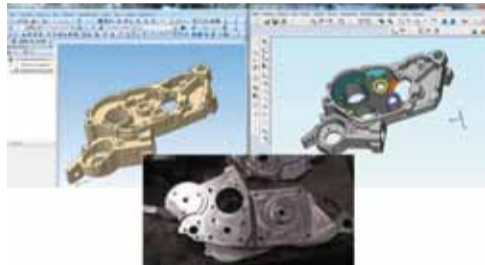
Конструкторско-технологическое проектирование корпуса редуктора и корпус редуктора, произведенный на 3-х координатном вертикально-фрезерном станке
